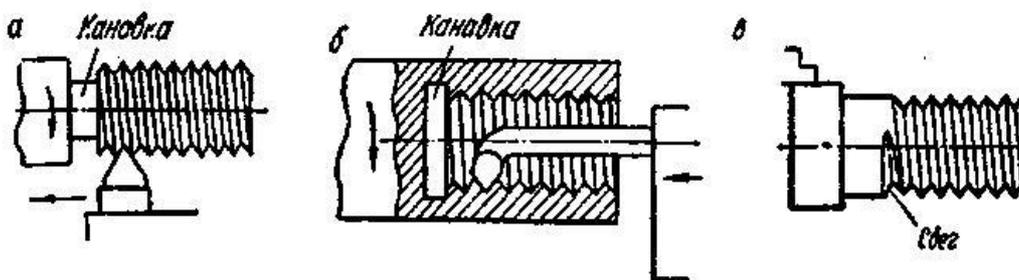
Канавки для выхода резца (а, б) и сбеги резьбы (в)
